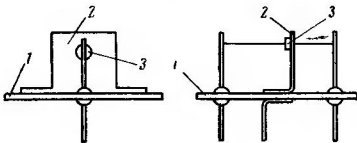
Конструкция транзистора: 1 — основание корпуса транзистора; 2 — стойка; 3 — монокристалл
